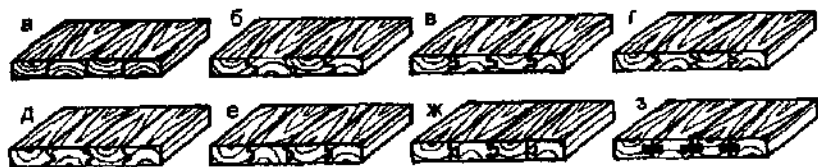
Боковые соединения заготовок: а — на гладкую фугу; б — в четверть; соединения в паз и гребень: в — прямоугольный; г — треугольный; д — трапецидальный; е — овальный; ж — «ласточкин хвост»; з — на рейку
